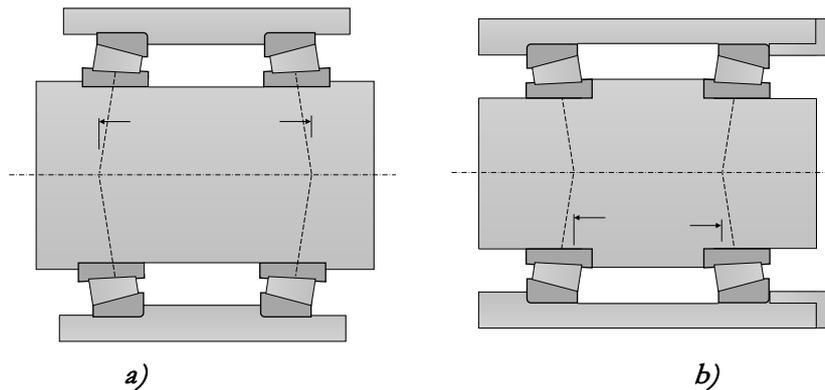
Montajes con rodamientos de rodillos cónicos: a) montaje indirecto b) montaje directo.
